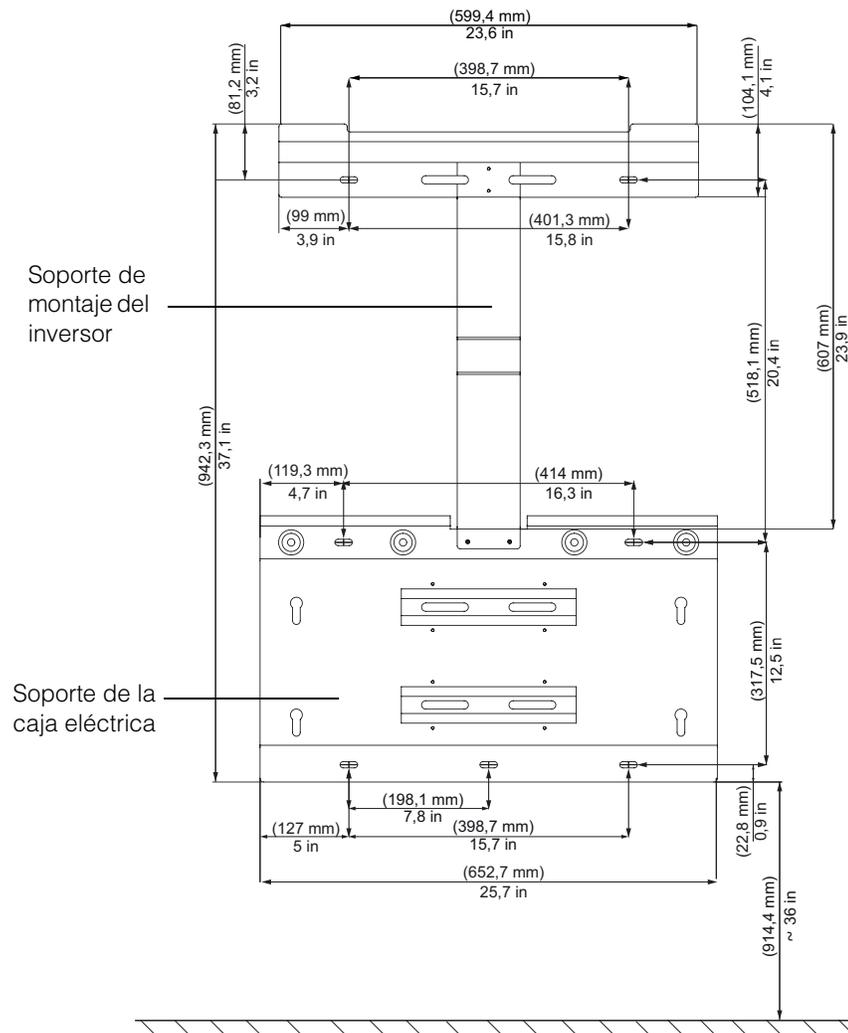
Dimensiones de los soportes de montaje: caja eléctrica e inversor
